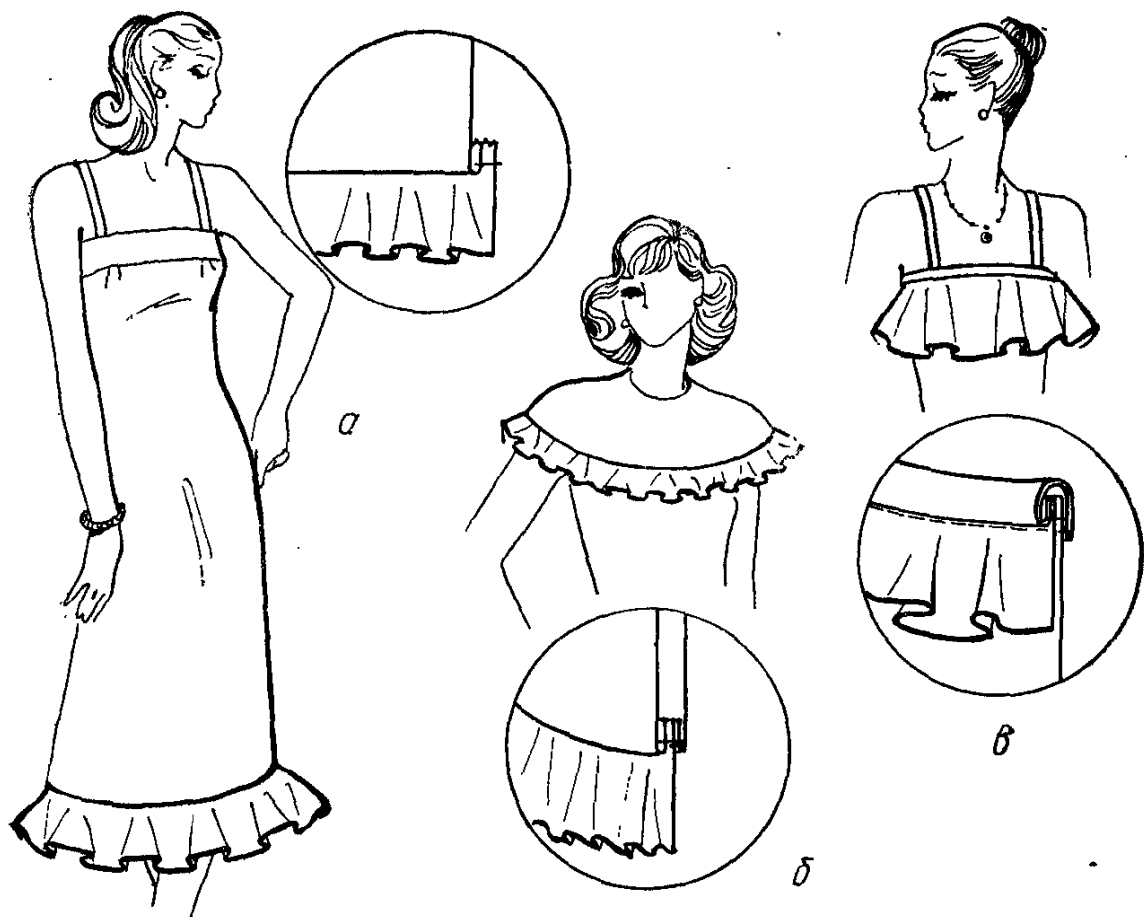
Соединение оборок, расположенных по краю детали, с основной деталью
